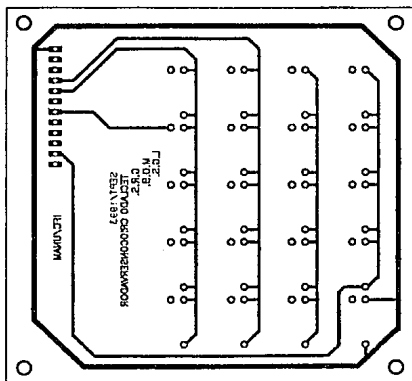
Cara de soldadura del circuito impreso del teclado.
